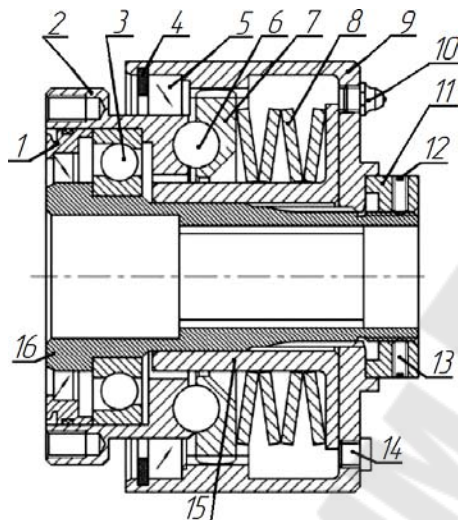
Муфта шнека предохранительная: 1 – крышка; 2 – стакан; 3 – подшипник; 4, 12 – кольца стопорные; 5 – манжета; 6 – шарик; 7 – диск; 8 – пружина; 9 – корпус; 10 – масленка; 11 – гайка; 13 – винт; 14 – клапан предохранительный; 15 – втулка; 16 – вал шлицевой
